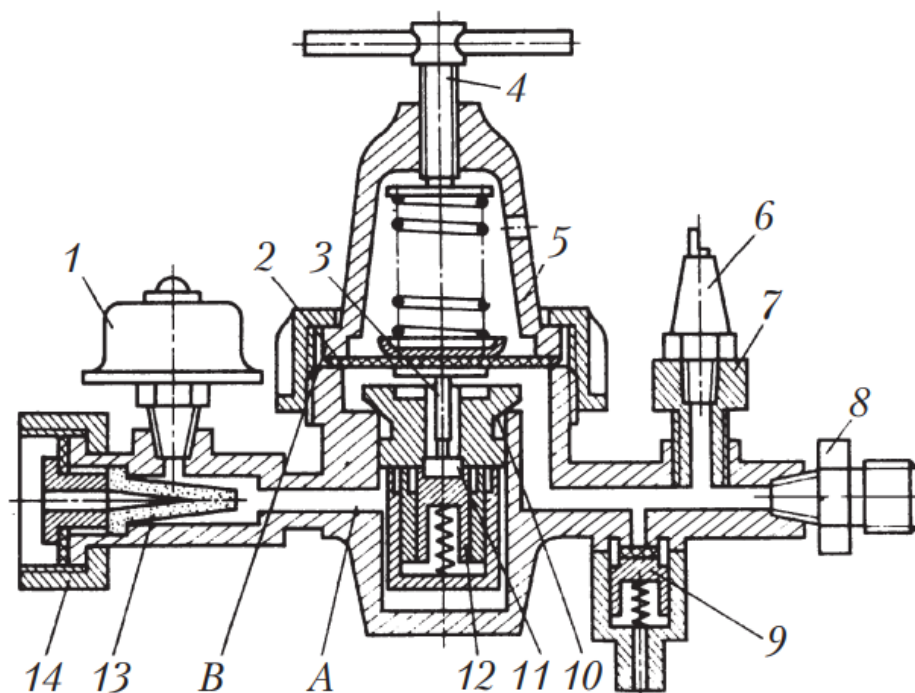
Схема редуктора высокого давления: 1 — датчик манометра высокого давления; 2 — мембрана; 3 — толкатель; 4 — регулировочный винт; 5 — крышка; 6 — сигнализатор падения давления; 7 — переходник; 8 — выходной штуцер; 9 — предохранительный клапан; 10 — седло; 11 — дополнительный фильтр; 12 — редуцирующий клапан; 13 — керамический фильтр; 14 — гайка; А — камера высокого давления; В — рабочая камера
